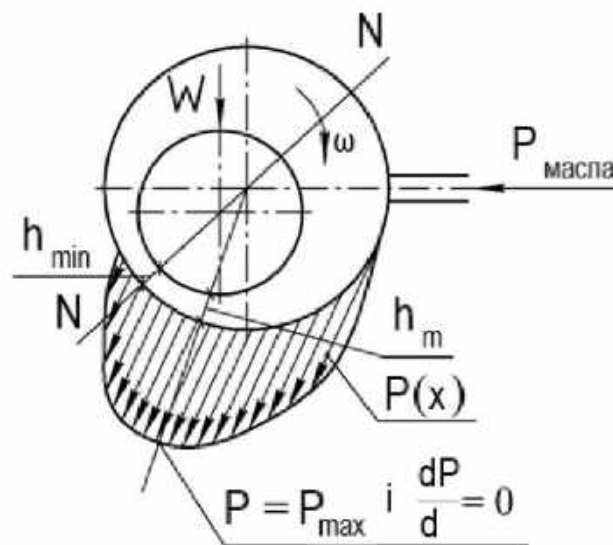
Стан гідродинамічного підшипника після спливання вала
